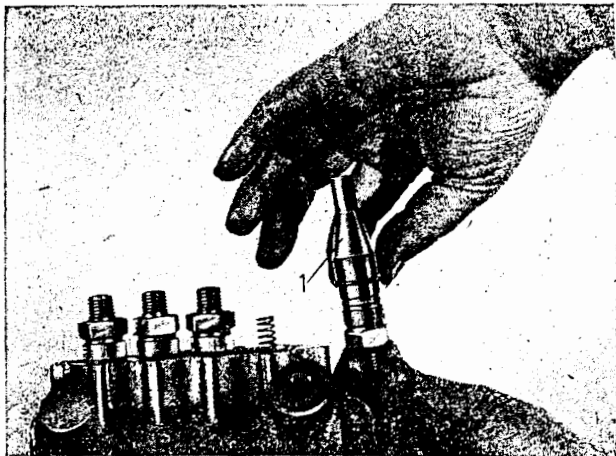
Rundring mit Aufzieher (1) (Werkzeug Nr. W 116) aufziehen
